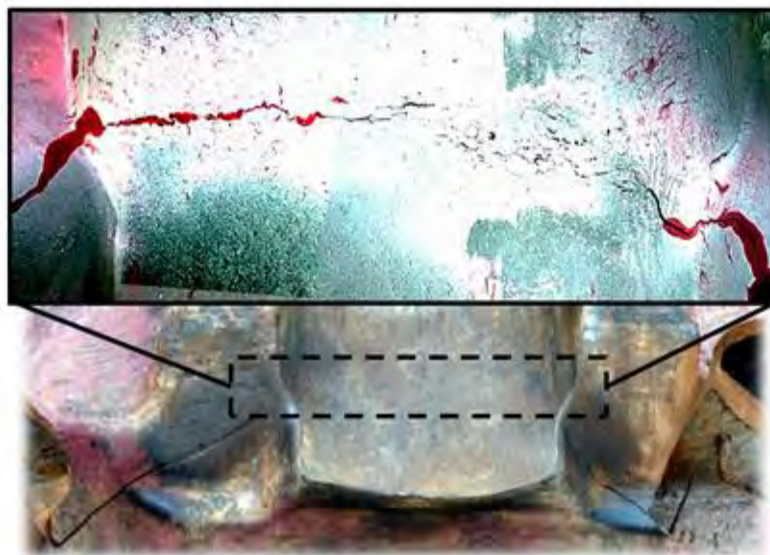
Extensión de la Fisura 1 en el apoyo del rodillo.
